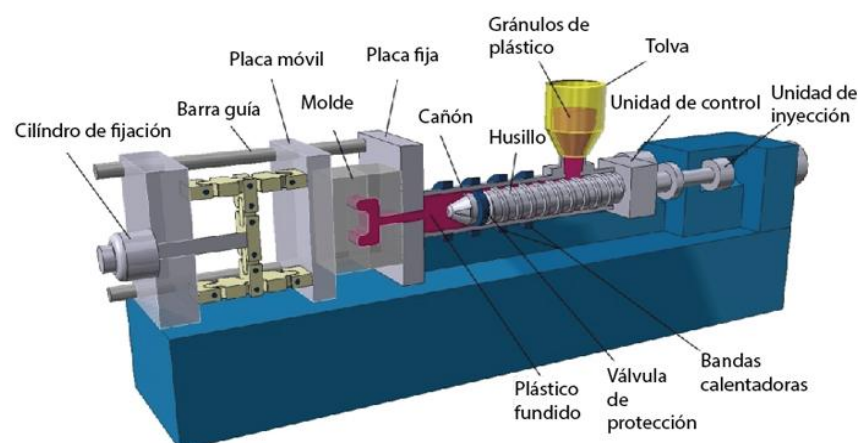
Màquina d'emmotllament per injecció. Parts. Font: Protomold
